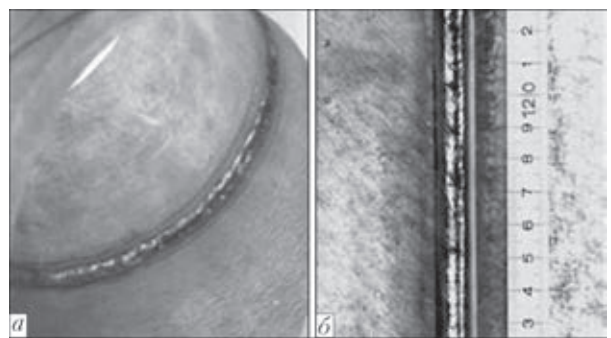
Блестящий гладкий валик на обратной (а) и лицевой (б) поверхности корневого шва (сталь 304, пруток TG-X308L)
